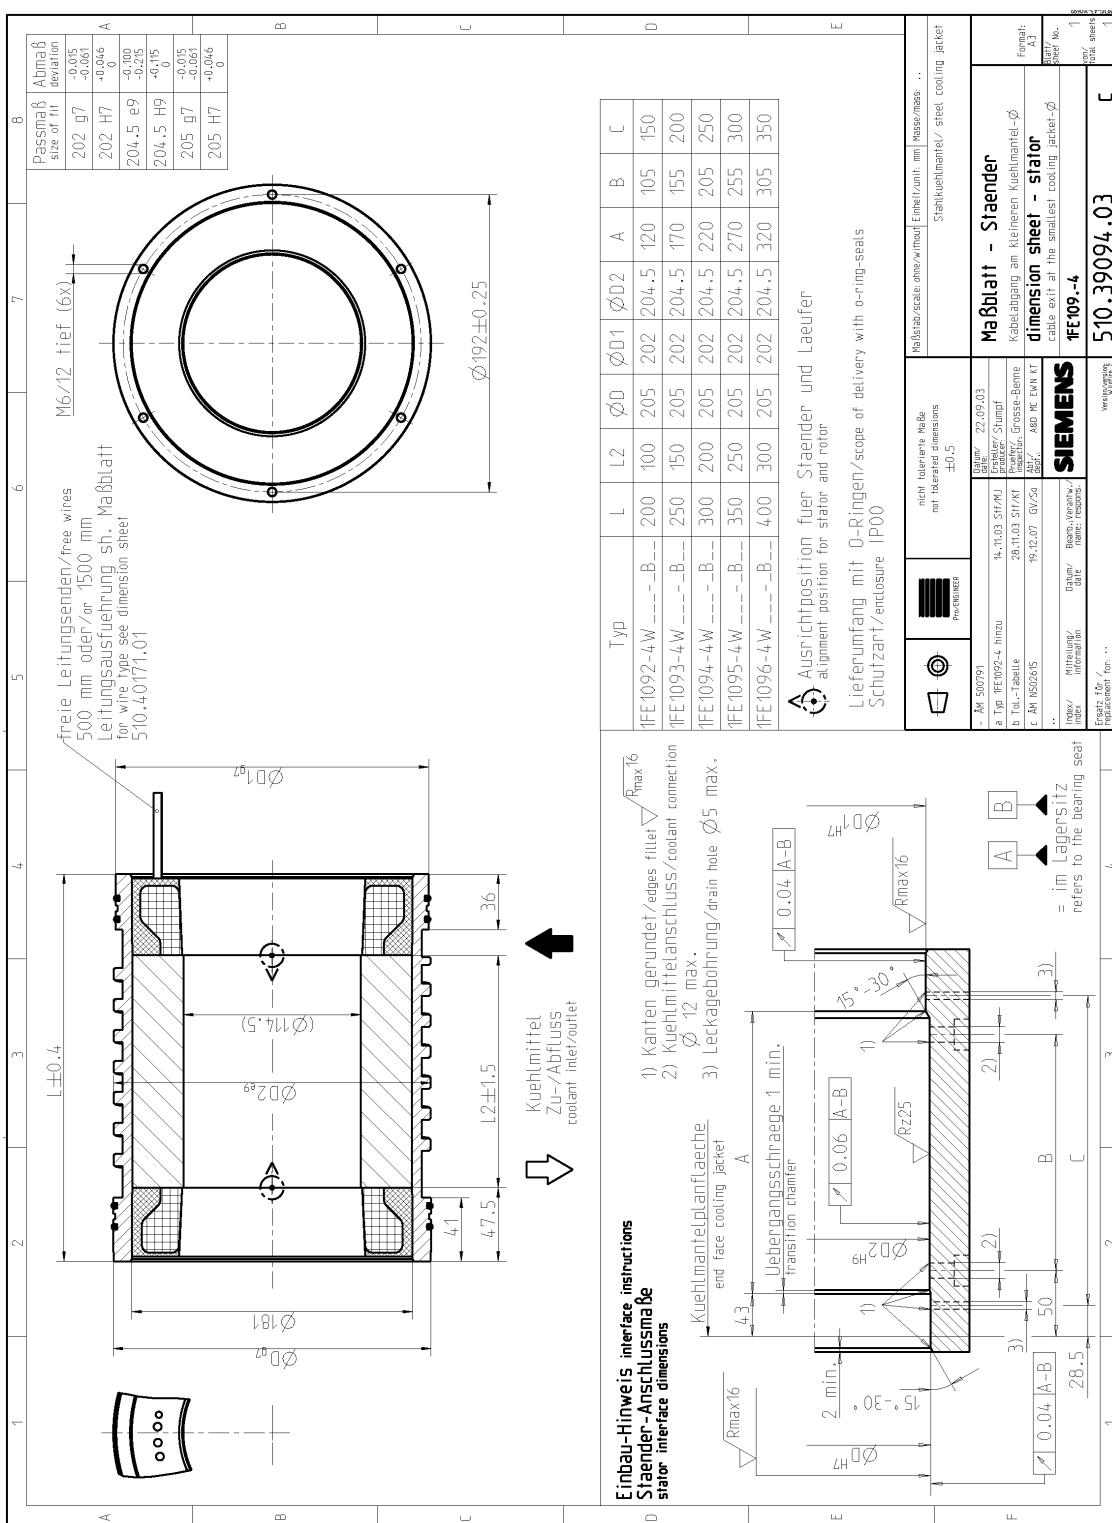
1FE109-4, Ständer mit Kühlmantel, Kabelabgang am kleineren Kühlmanteldurchmesser
